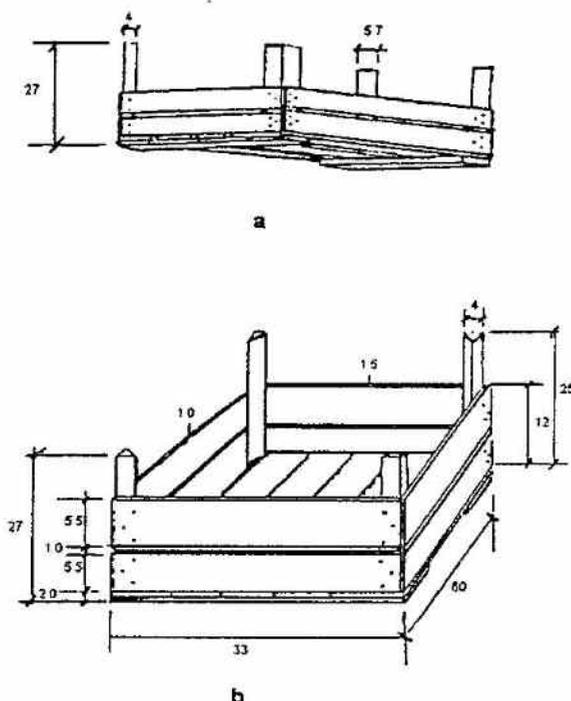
Dimensões e detalhes de caixa de madeira utilizada para o transporte de pencas de banana: a) vista inferior; b) vista superior.
